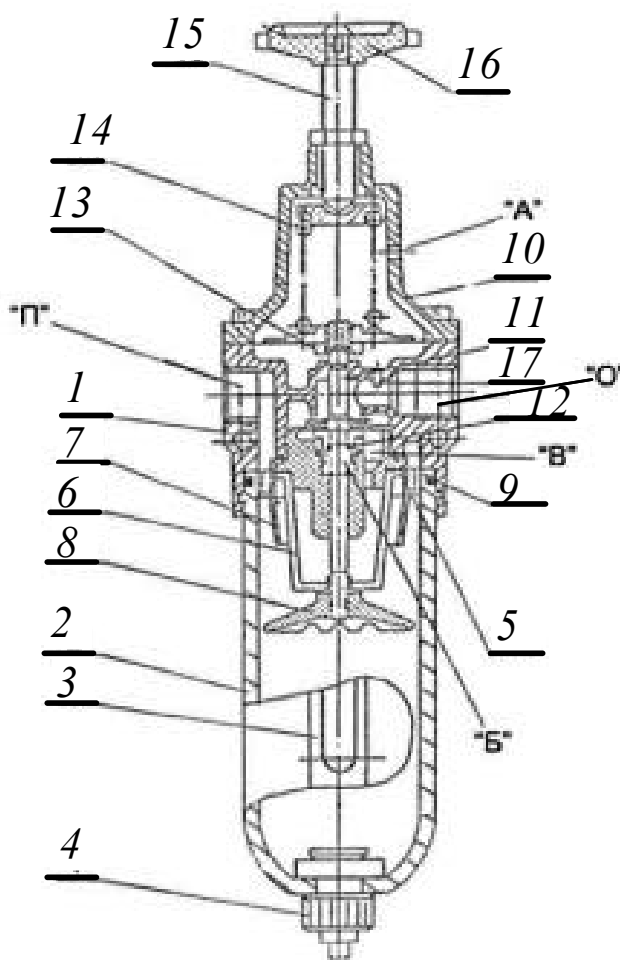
Блок підготовки повітря: 1 – корпус; 2 – резервуар для конденсату; 3 – прозоре вічко; 4 – конденсатовідвідник; 5 – крильчатка; 6 – елемент; 7 – дефлектор; 8 – заслінка; 9 – гумове кільце; 10 – склянка; 11 – дросельний клапан; 12 – пружина; 13 – мембранний вузол; 14 – навантажувальна пружина; 15 – навантажувальний гвинт; 16 – ручка; 17 – трубка, яка з'єднує підмембранну камеру та вихідний отвір «О»
